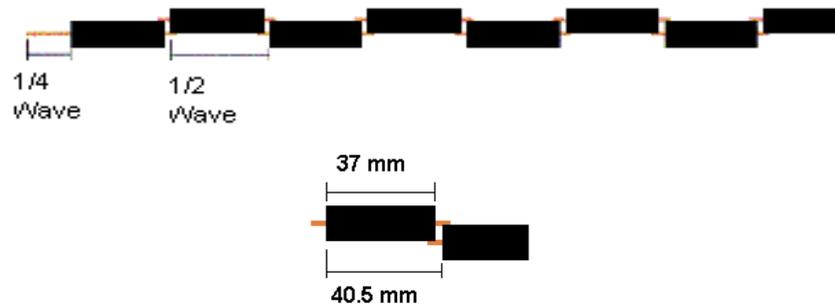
Medidas de los segmentos soldados de una antena coaxial.
